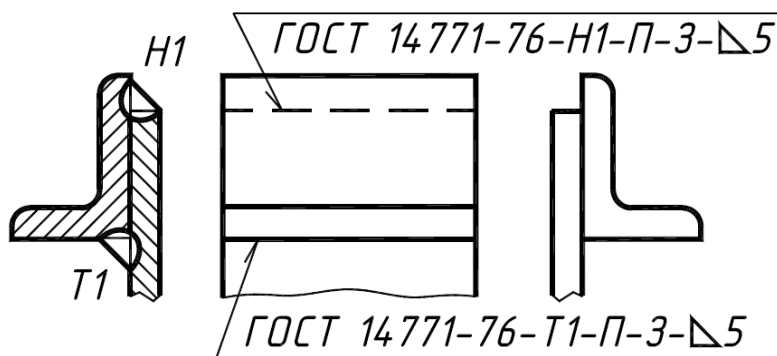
Нанесение условных обозначений сварных швов.
